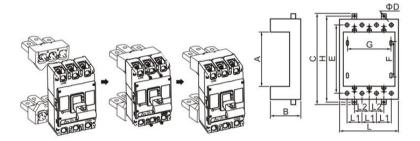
Габаритные и установочные размеры заднего втычного присоединения КА-330E
